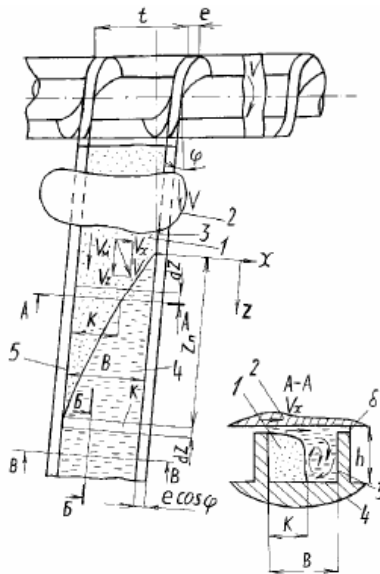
Схема руху термопластичного матеріалу в зоні плавлення: 1 – твердий матеріал (пробка); 2 – корпус; 3 – штовхальна стінка нарізки шнека; 4 – зона розплаву; 5 – пасивна стінка каналу
